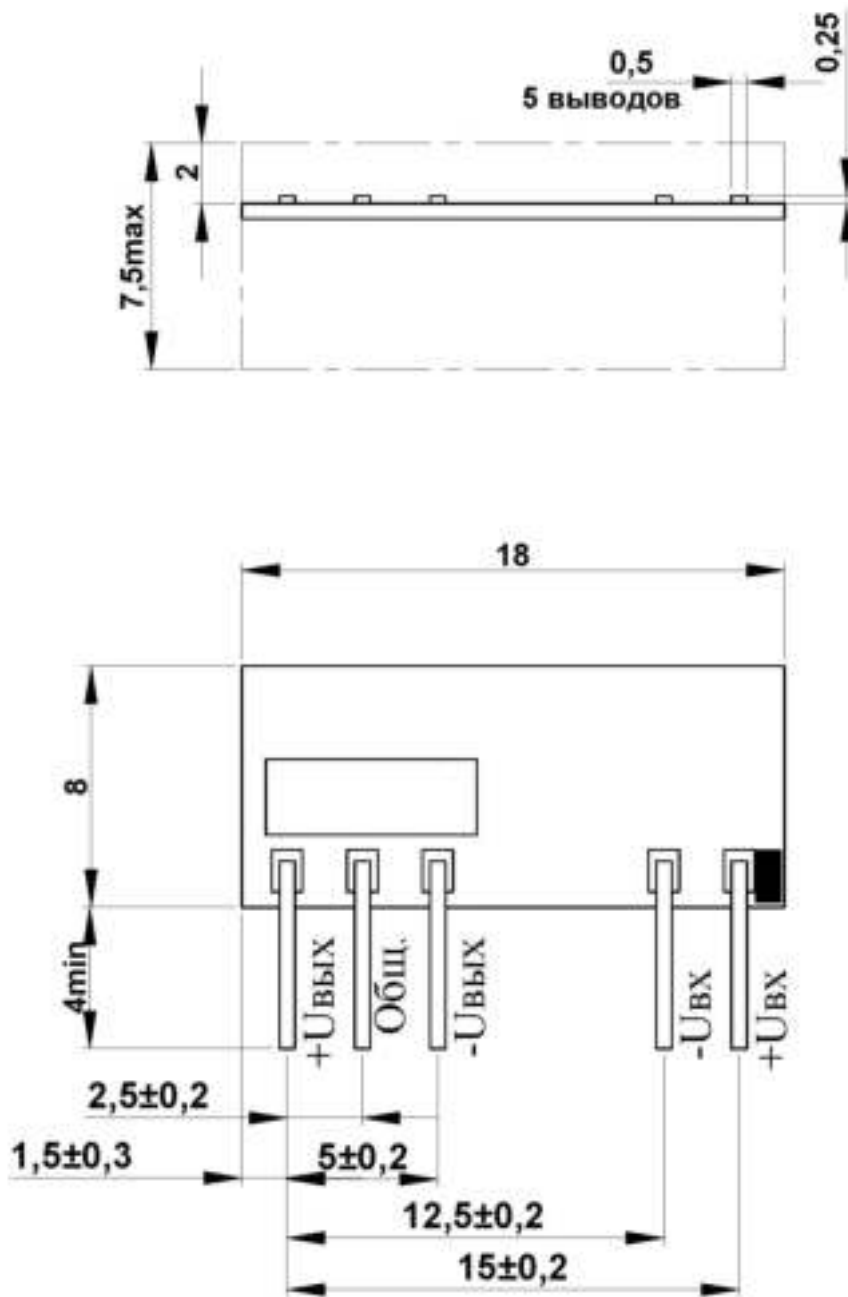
Габаритный чертеж модулей в конструктивном исполнении «В»
